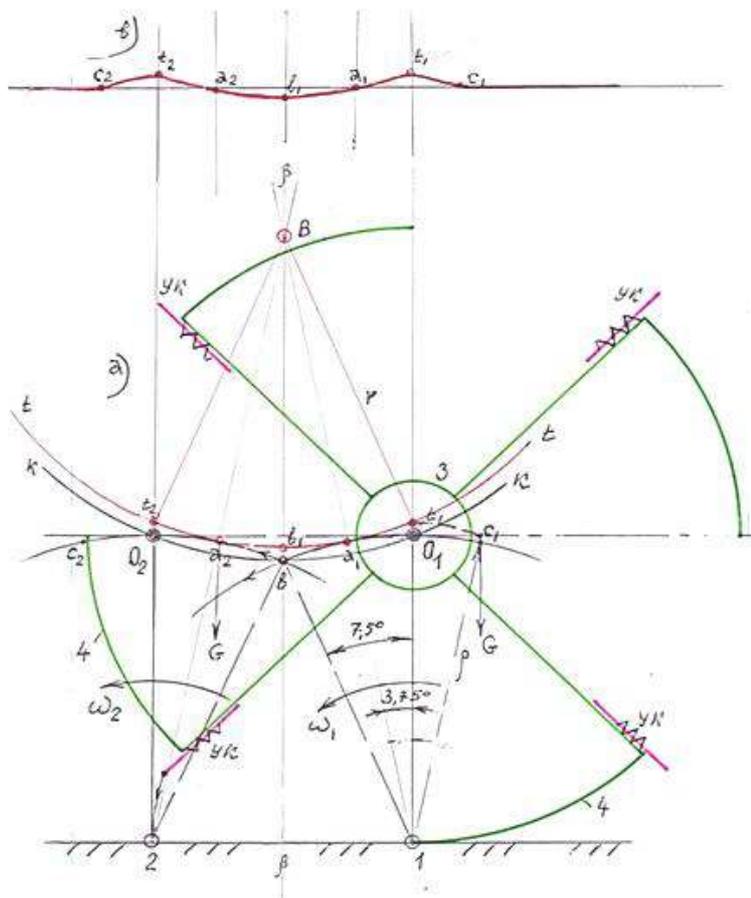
Конструктивная схема четырехного шагающего колеса
